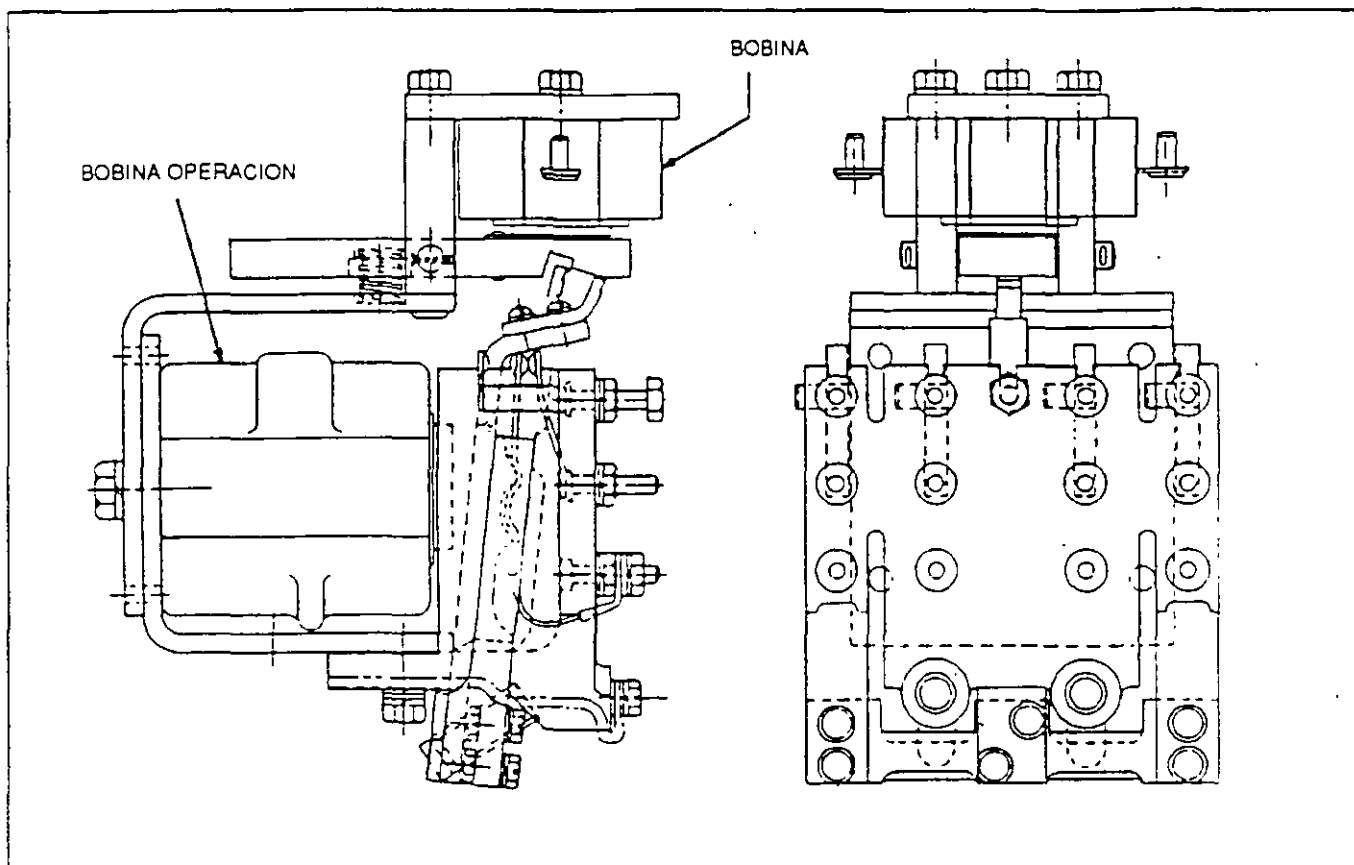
RELEVADOR DE TRABAMIEN TO LV67. E-39102-S
